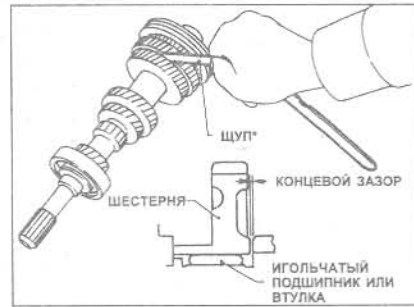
Измерение бокового люфта шестерни - показана шестерня 5-ой передачи входного вала (Глава 8)
